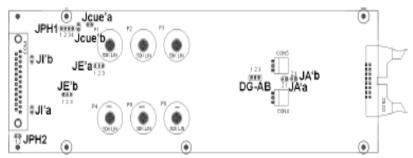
Módulo de micrófono 2810 (vista lado soldaduras)
